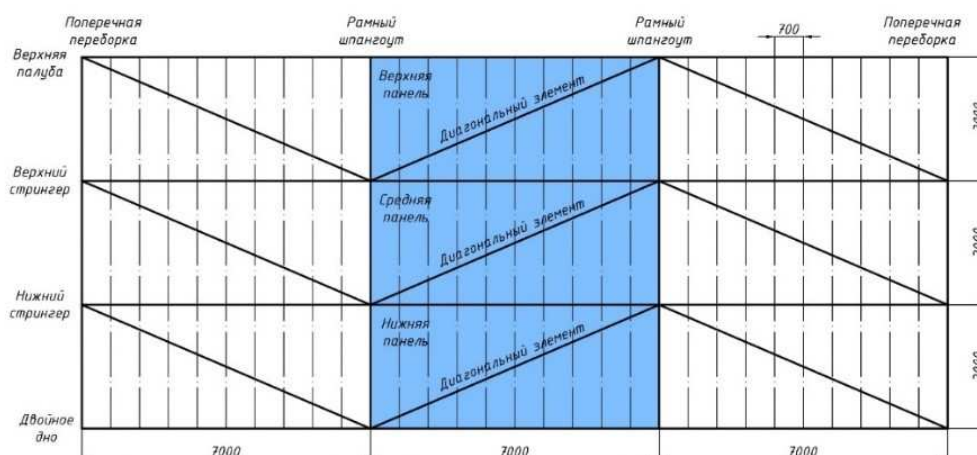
Расчетная схема бортового перекрытия набранного по поперечной системе набора с диагональными элементами [2]
